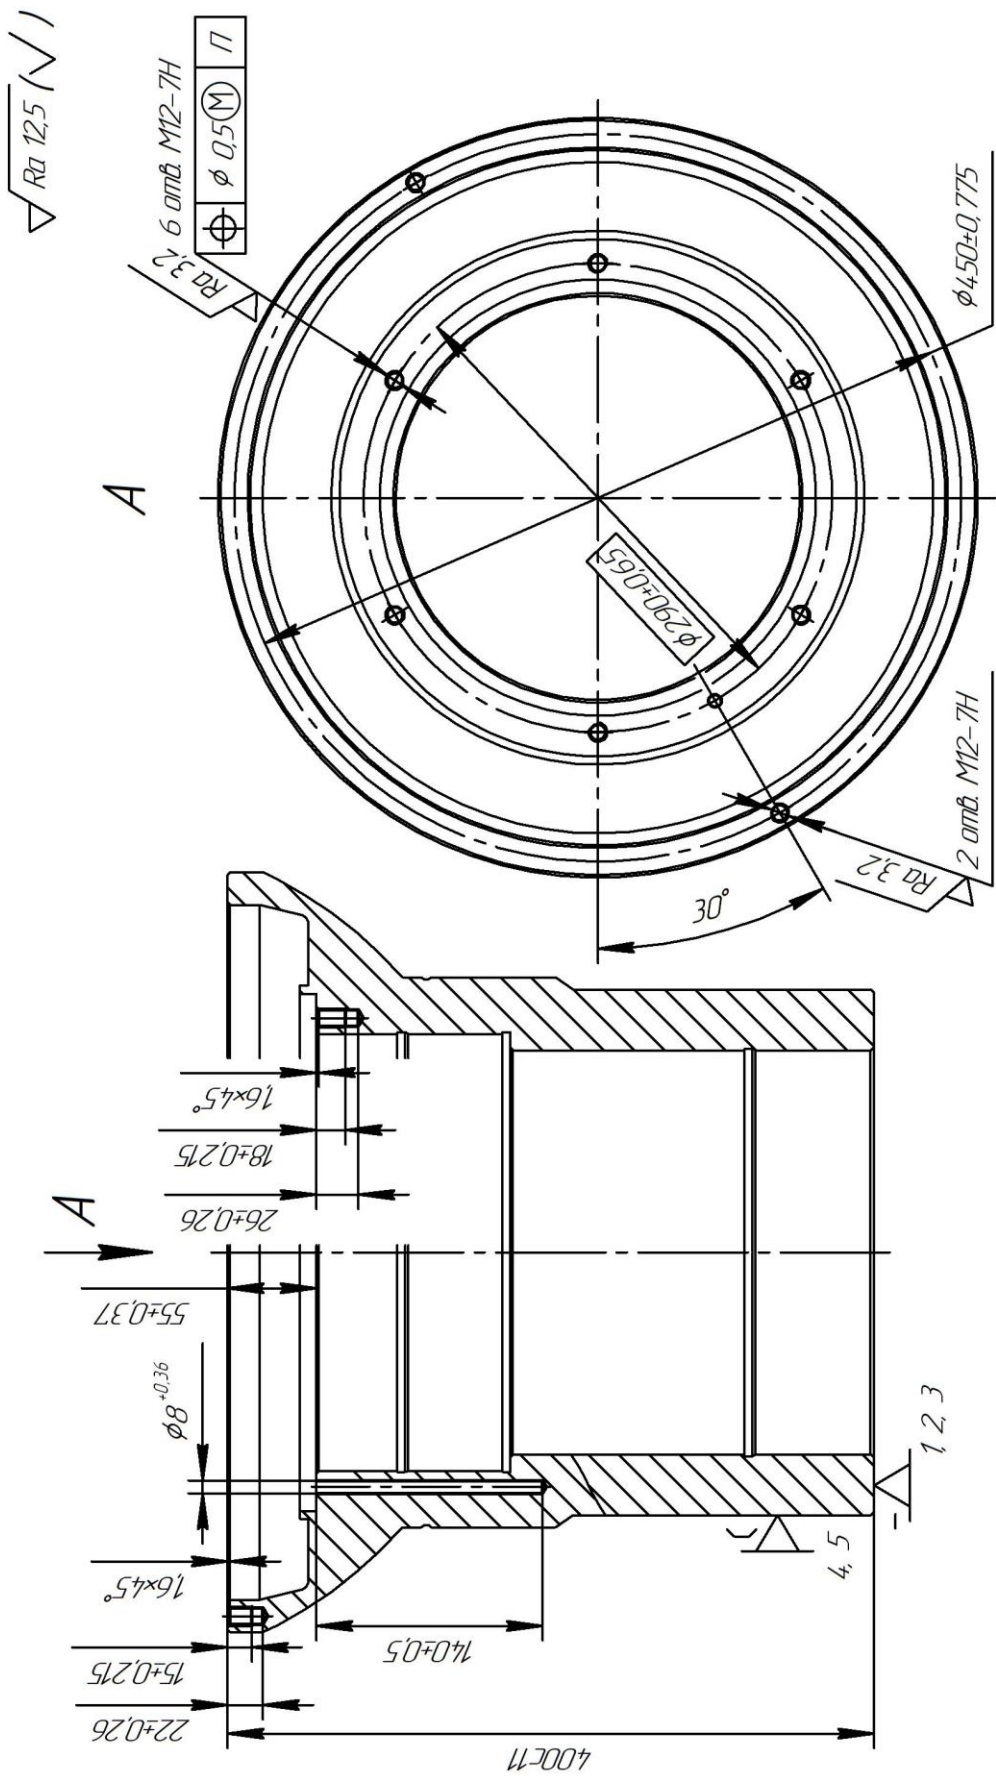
Схема базування заготовки на операції радіально-свердильній 050 (установ А)
